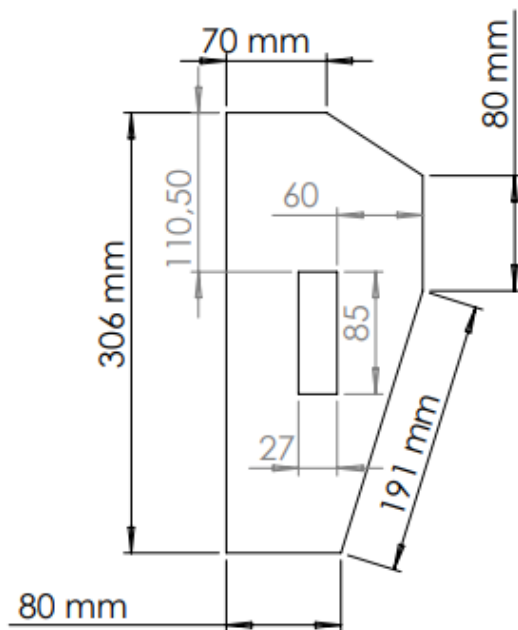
Tapa lateral derecha e izquierda Fuente: Autores
